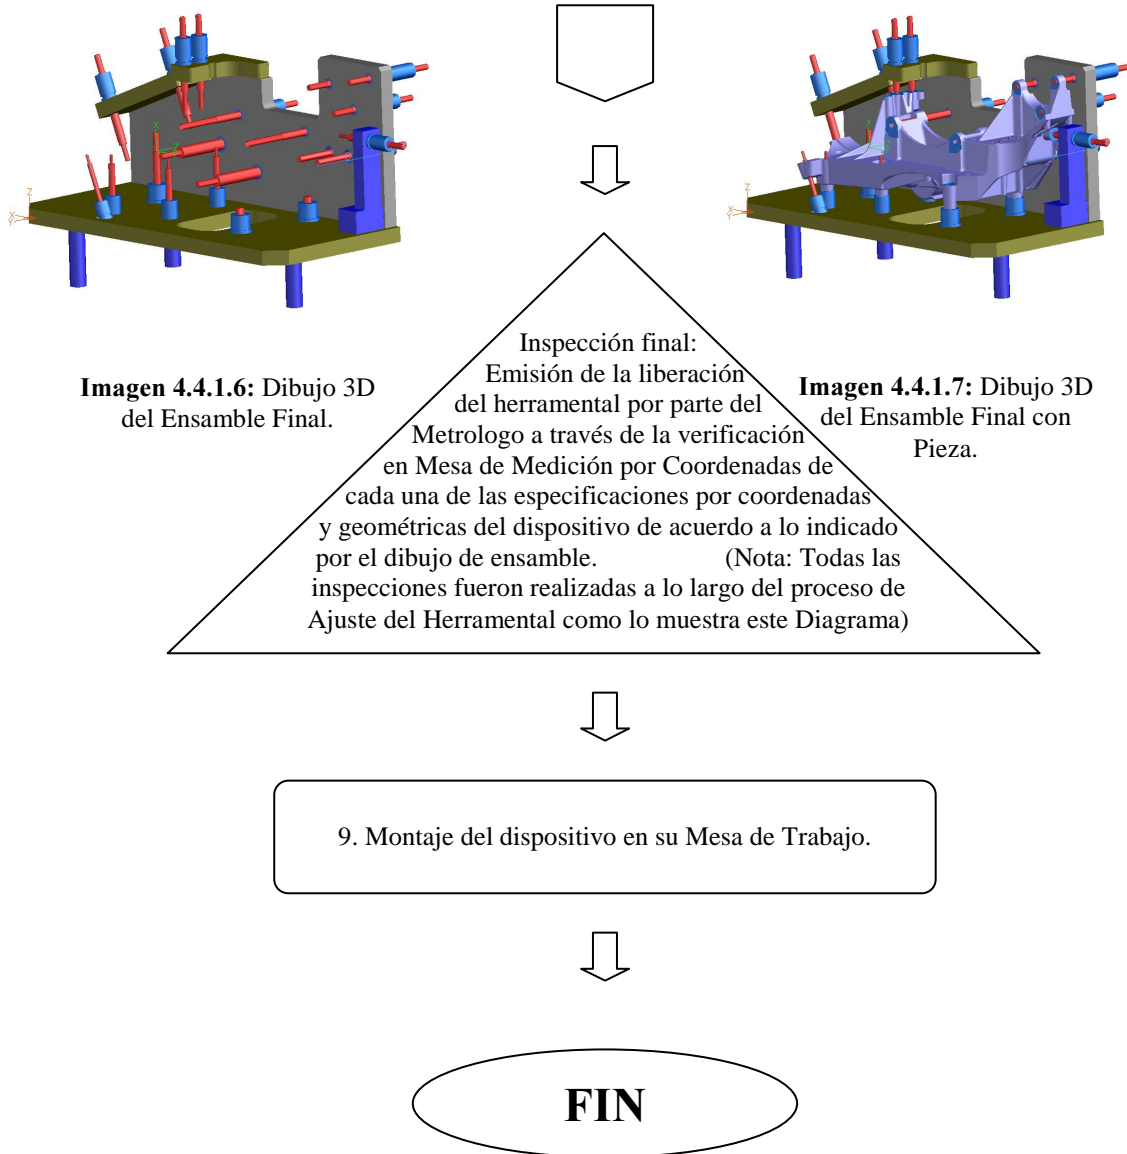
Dibujo 3D del Ensamble Final.
